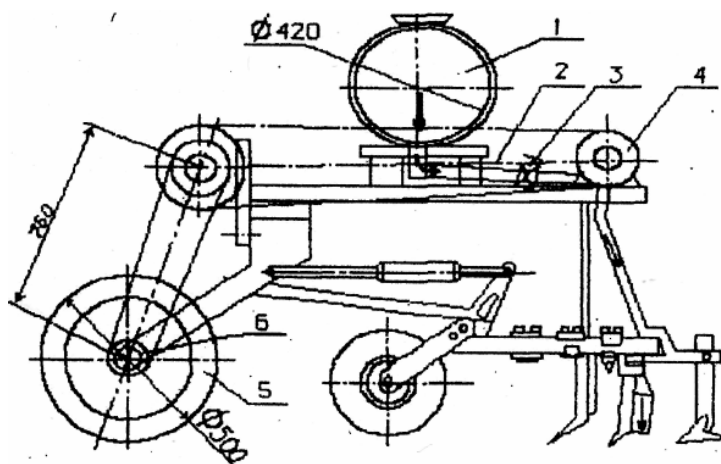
Схема установки пружинного рабочего органа для внесения ЖКУ на культиваторе КРН - 5,6 (Чувашская АССР):
